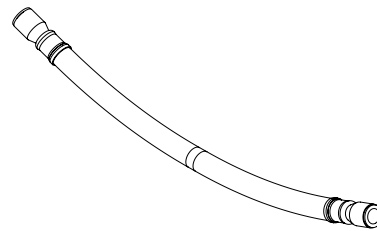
Flexibler Schlauch mit Steckanschluss.
